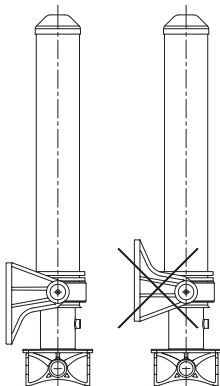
Montaje del soporte del chasis del cilindro tipo H
